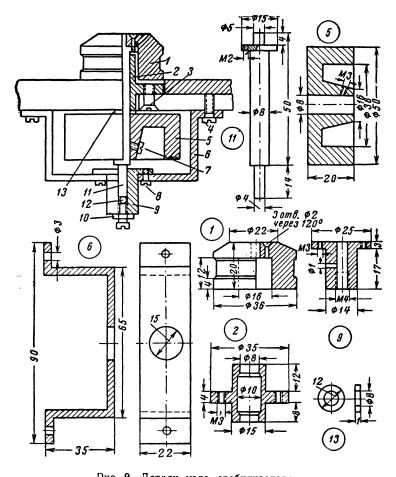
Детали узла стабилизатора. 1— дюралюминиевый ролик; 2— латунная втулка; 3— винты с потайной головкой МЗ × 8 (3 шт); 4— винты МЗ ×8(2 шт.); 5— стальной маховик; 6— стальная скоба; 7— упорый винт МЗ × 5; 8— винты МЗ 5(3 шт.); 9— упорная втулка из латуни; 10— винт М4×10 с гайкой; 11— стальная ось; 12— стальной шарик диаметром 3 мм; 13— стальная шайба.
